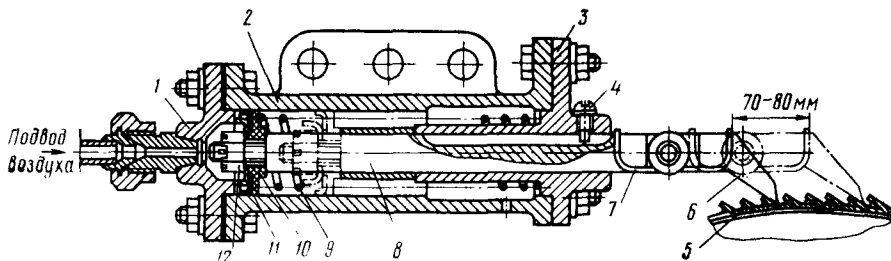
Механизм привода вращающейся кассеты воздухоочистителя:
